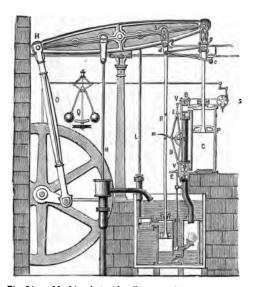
Machine à double effet de Boulton et Watt, 1784.
